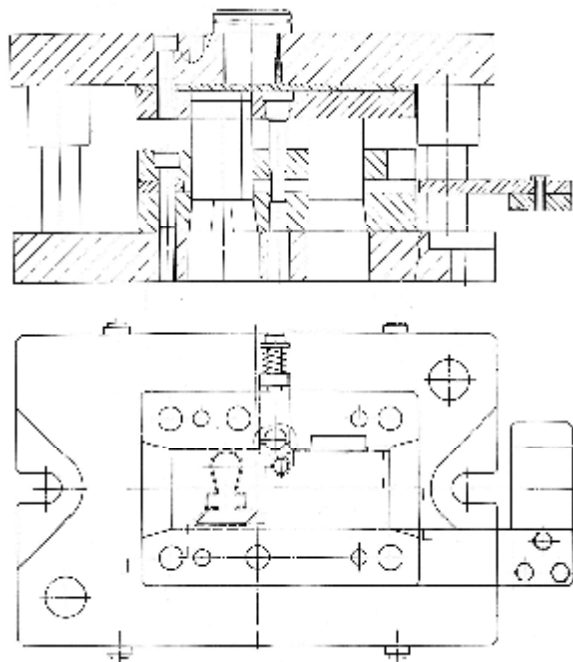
Штамп для виготовлення деталей на ОАО «Кредмаш»
